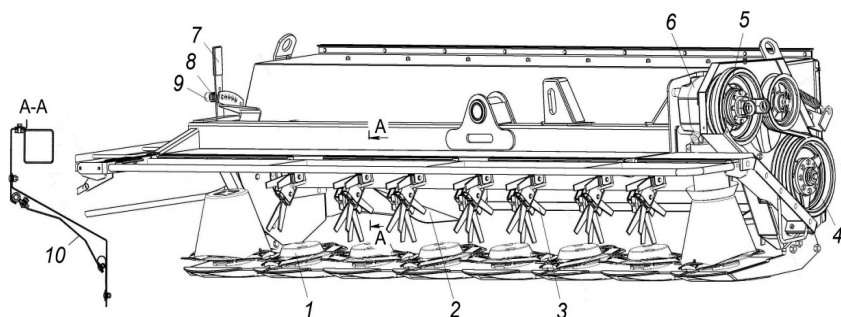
Боковая секция: 1 – режущий брус; 2 – валкообразователь; 3 – ротор плющильного аппарата; 4, 5 – шкивы ременной передачи; 6 – редуктор; 7 – рычаг; 8 – пружина; 9 – ручка; 10 – дека
